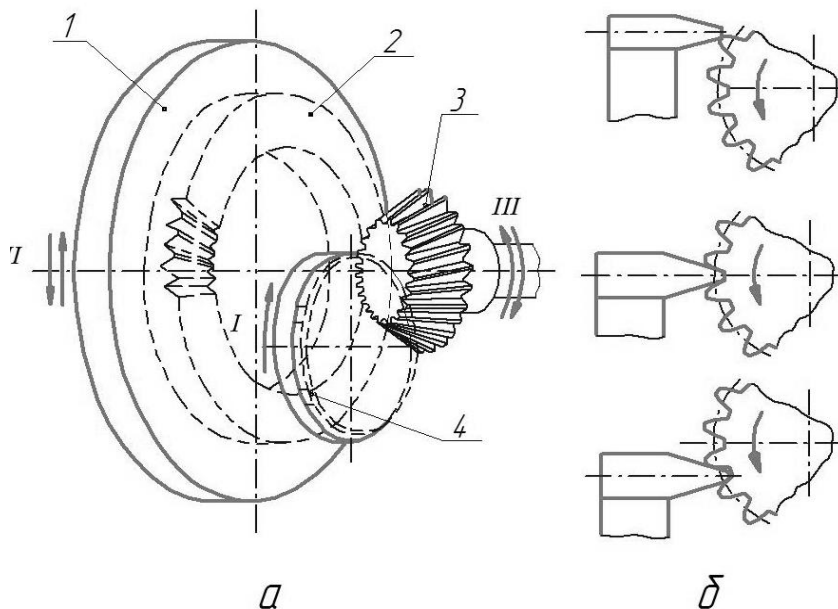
Схема нарізування зубчастих коліс з криволінійними зубами торцевою зуборізною головкою
